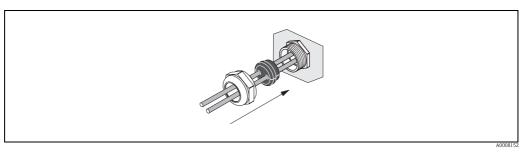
Pressacavo per due cavi di collegamento (2 x Ø 4 mm) per ingresso cavo
